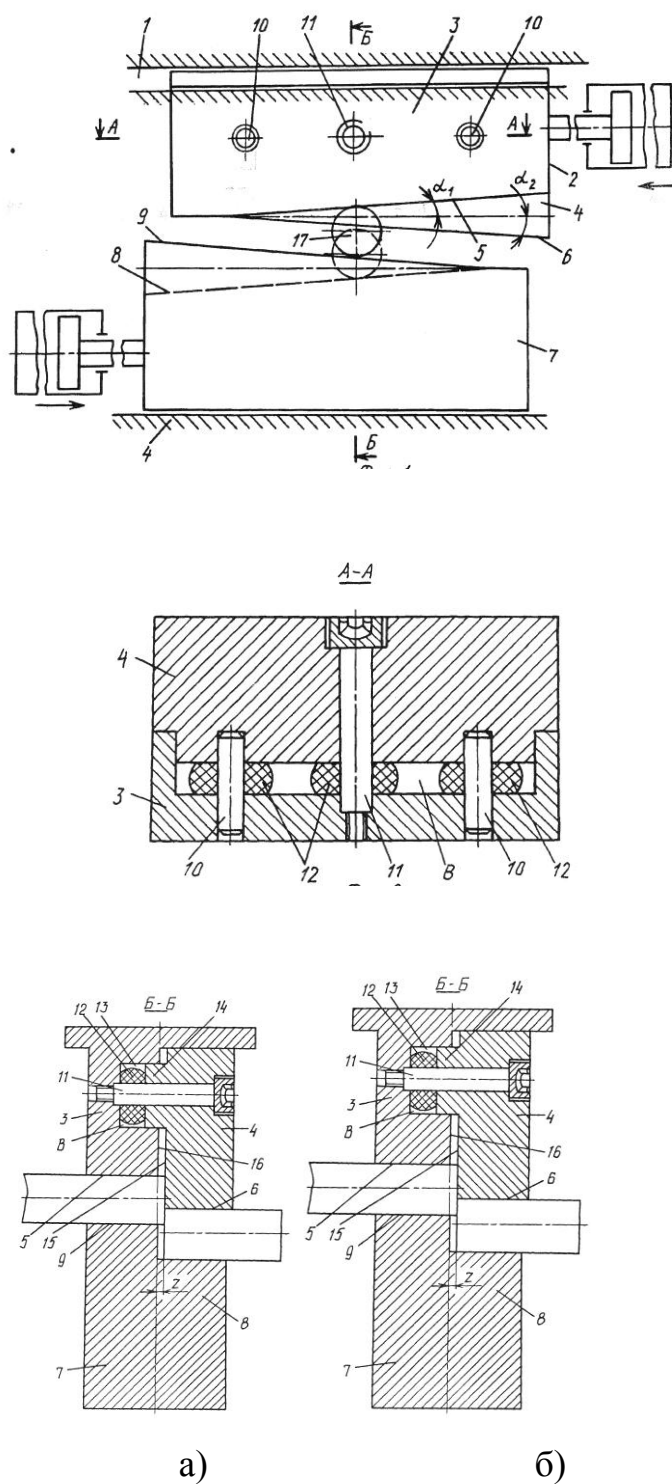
Ножи с устройством для регулировки осевого зазора:
